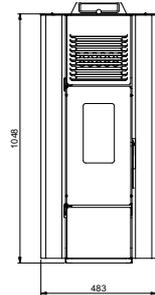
Dimensions générales: Mod 14KW /17KW
